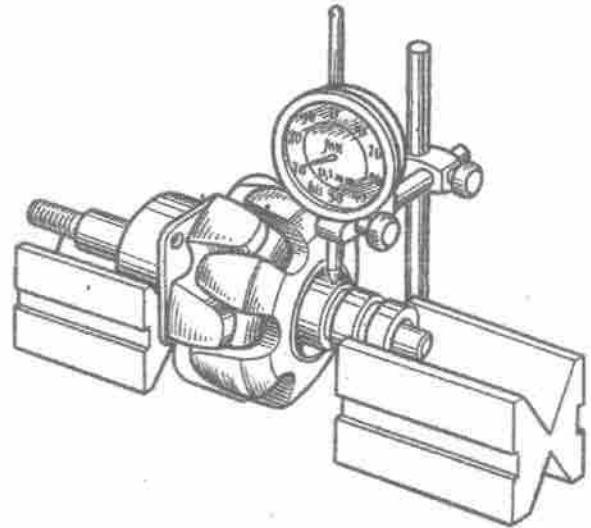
Prüfen des Rundlauffehlers der Schleifringe
